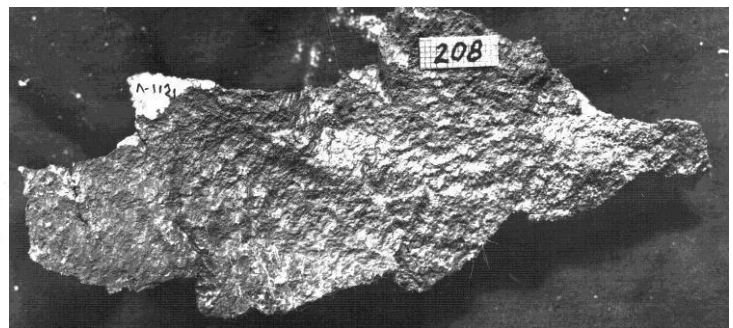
Сколювання робочого шару валка стану 1700 гарячої прокатки.
